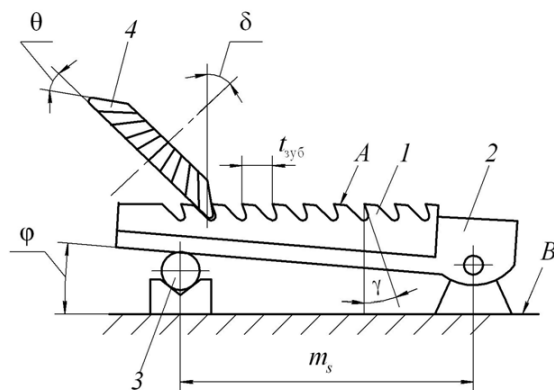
Схема фрезерования зубьев режущей части плоской протяжки:
